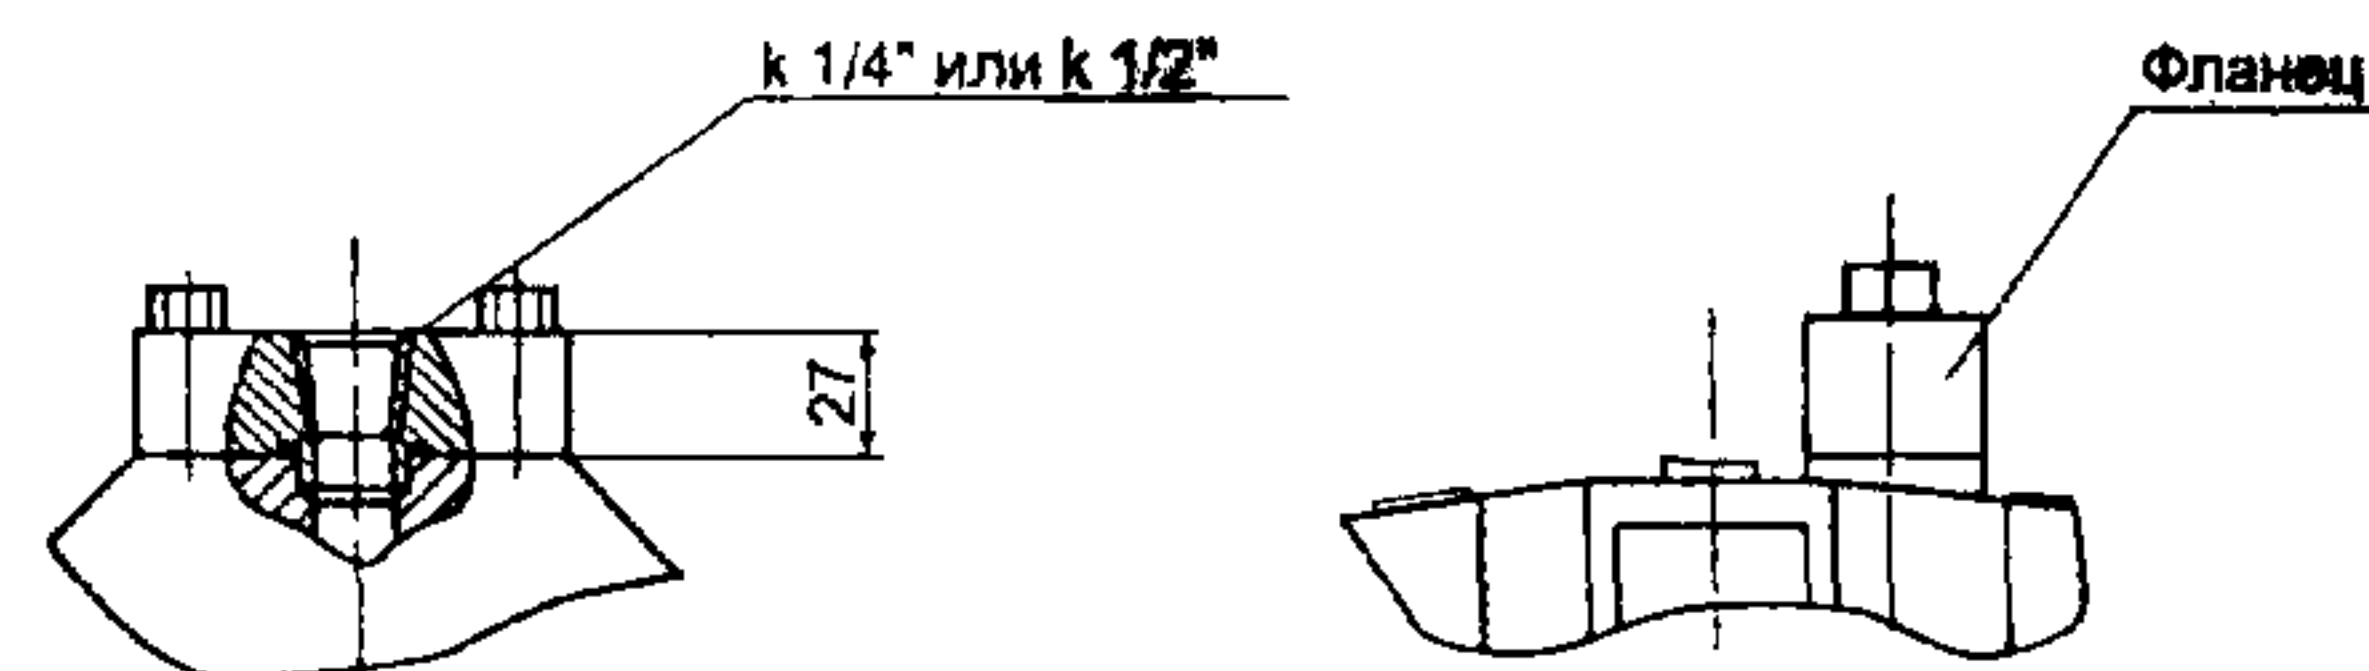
Установочные и присоединительные размеры преобразователей Сафир-22Р моделей 2051, 2161, 2171, 2351
